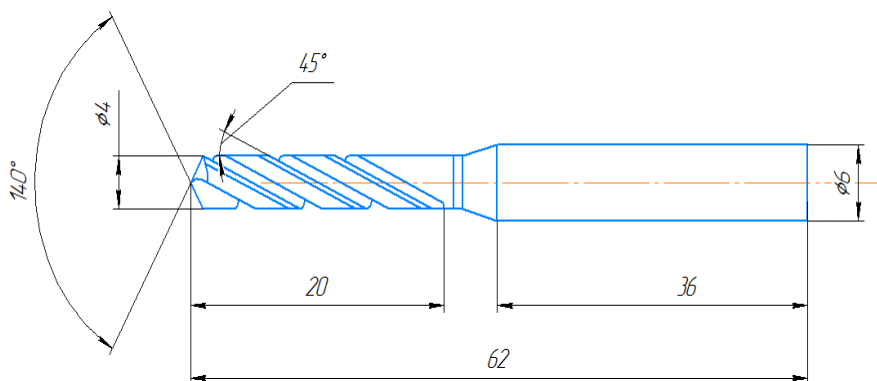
Эскиз режущего инструмента – сверла фирмы Iscar
